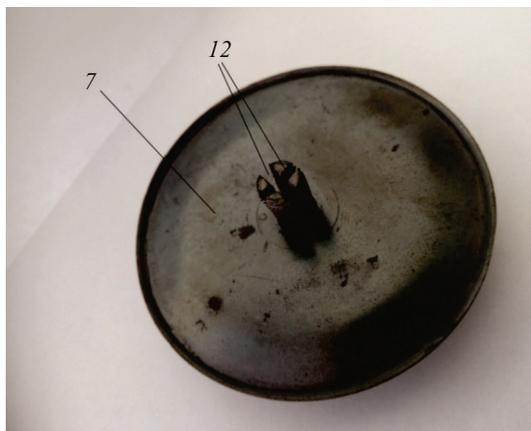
Крышка газовой горелки для бытовых плит с интенсификатором теплоотдачи в виде стержня с резьбой и увеличивающимися щелевыми зазорами (продольными разрезами)
